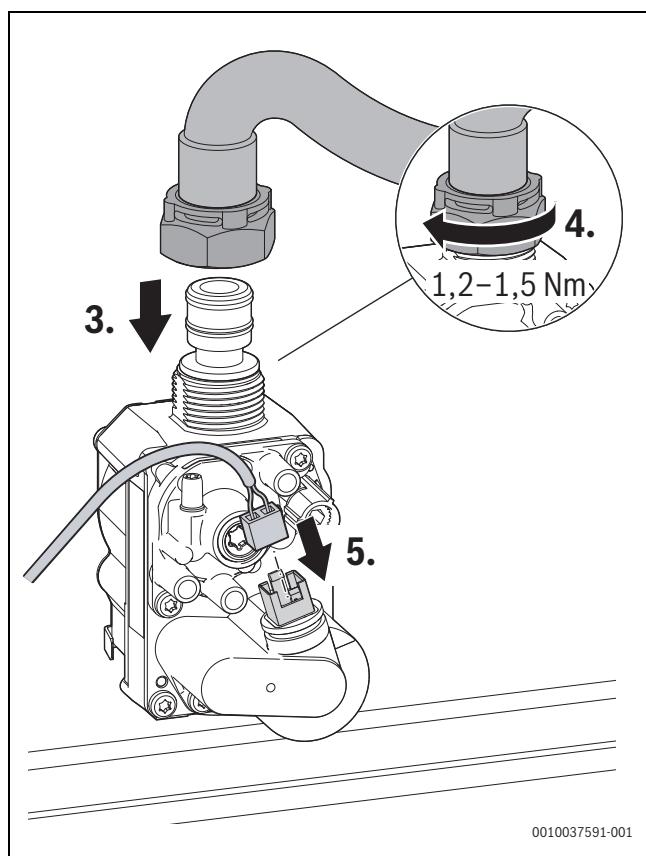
Gasschlauch und Stecker anschließen – Anzugsdrehmoment beachten
